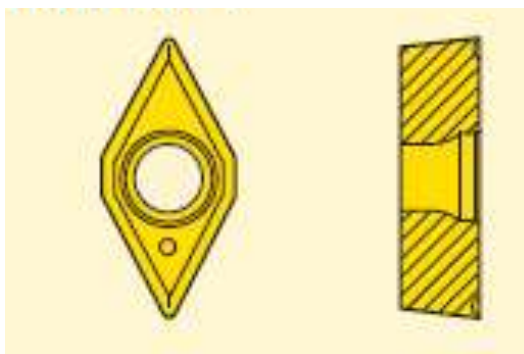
Пластина DCMT 11T032-FF1
